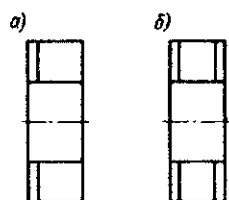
Подшипник с защитными шайбами: *a* — с одной; *б* — с двумя
